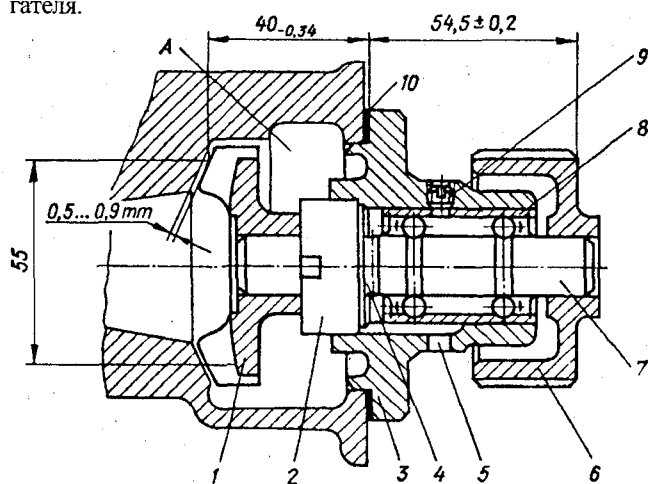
Водяной насос двигателя: 1 – крыльчатка; 2 – манжета; 3 – корпус; 4 – кольцевая канавка на валу; 5 – отверстие для слива жидкости; 6 – шкив водяного насоса; 7 – вал; 8 – шариковый подшипник; 9 – стопорный винт; 10 – прокладка; А – полость насоса
